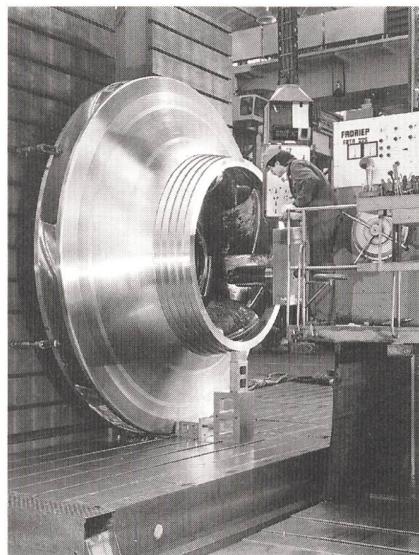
Moderne CNC-Maschine bei der Bearbeitung eines Pumpturbinen-Laufrades
